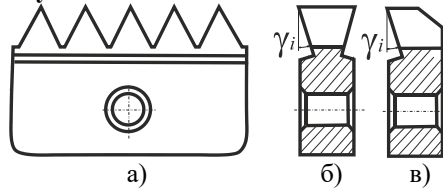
Основні типи твердосплавних непереточувальних пластинок гребінчастих фрез: б – двосторонніх, в – односторонніх
